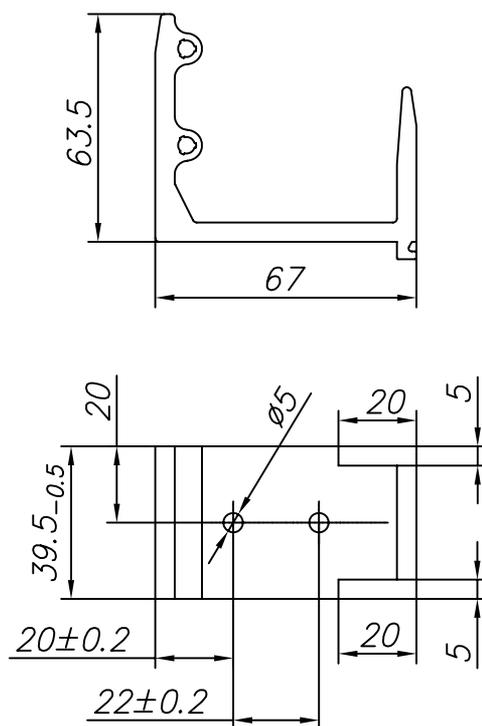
Изготовление соединителя FLGU.400.0912
